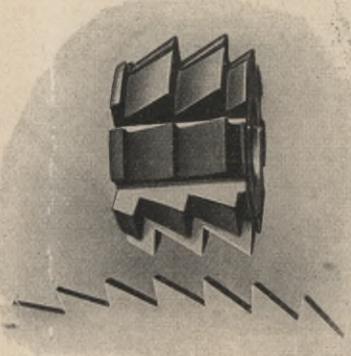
Mit dem Abwälzfräser gefrästes Kreissägeblatt
